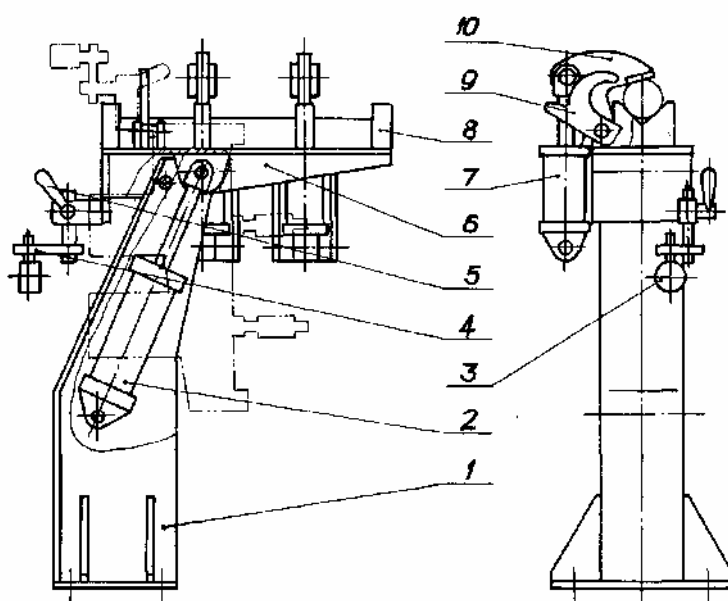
Стенд для узловой сборки коленчатого вала с маховиком и сцеплением: 1 – корпус; 2 и 7 – пневмоцилиндры; 3 – индикаторная головка; 4 – стойка; 5 – рукоятка; 6 – поворотная рама; 8 – призма; 9 – захват; 10 – рычаг
